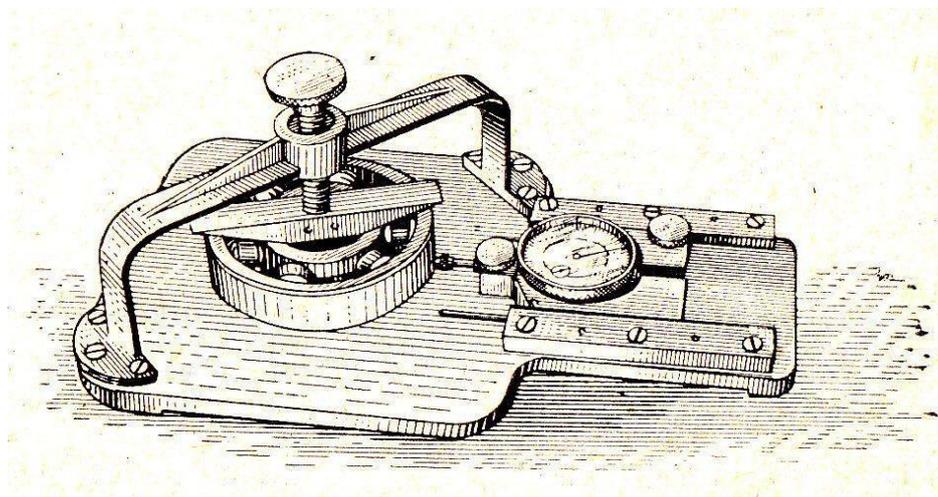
Прибор КИ-1223 для замера радиального зазора в подшипниках
